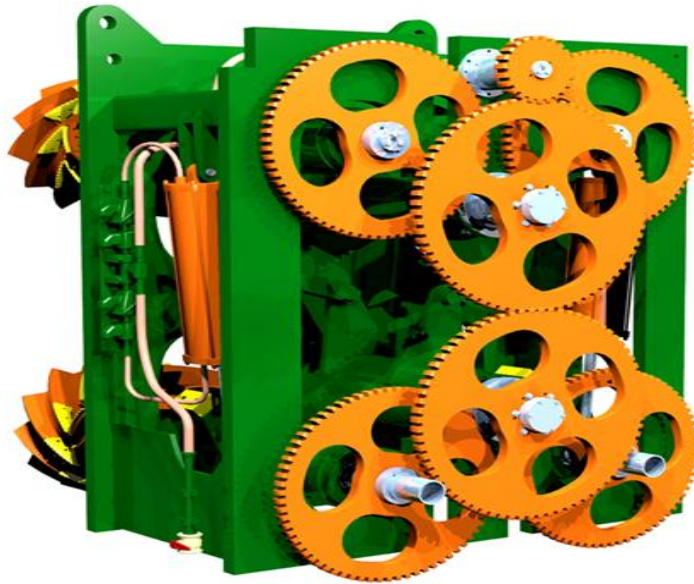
Engranajes descortezador (Fuente: Descortezador A8)
